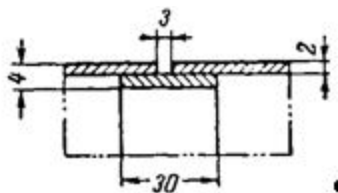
Подготовка к сварке продольных швов коробов круглого сечения
